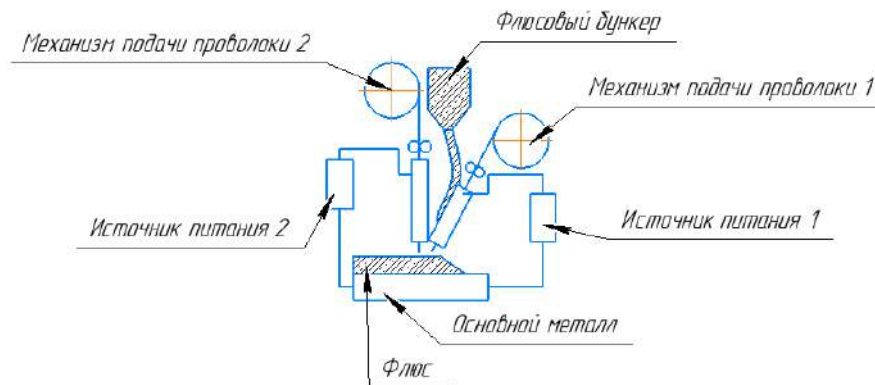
Схематическое изображение «Тандемной» сварки.
